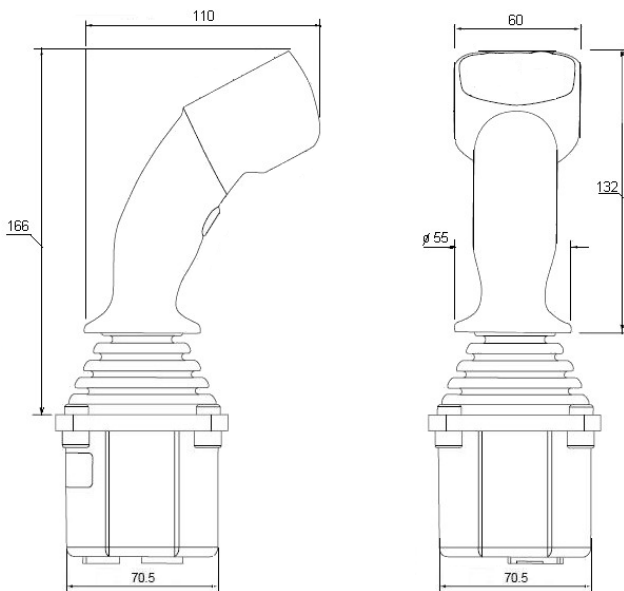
Габаритные размеры ДЖ и разметка места для его установки
